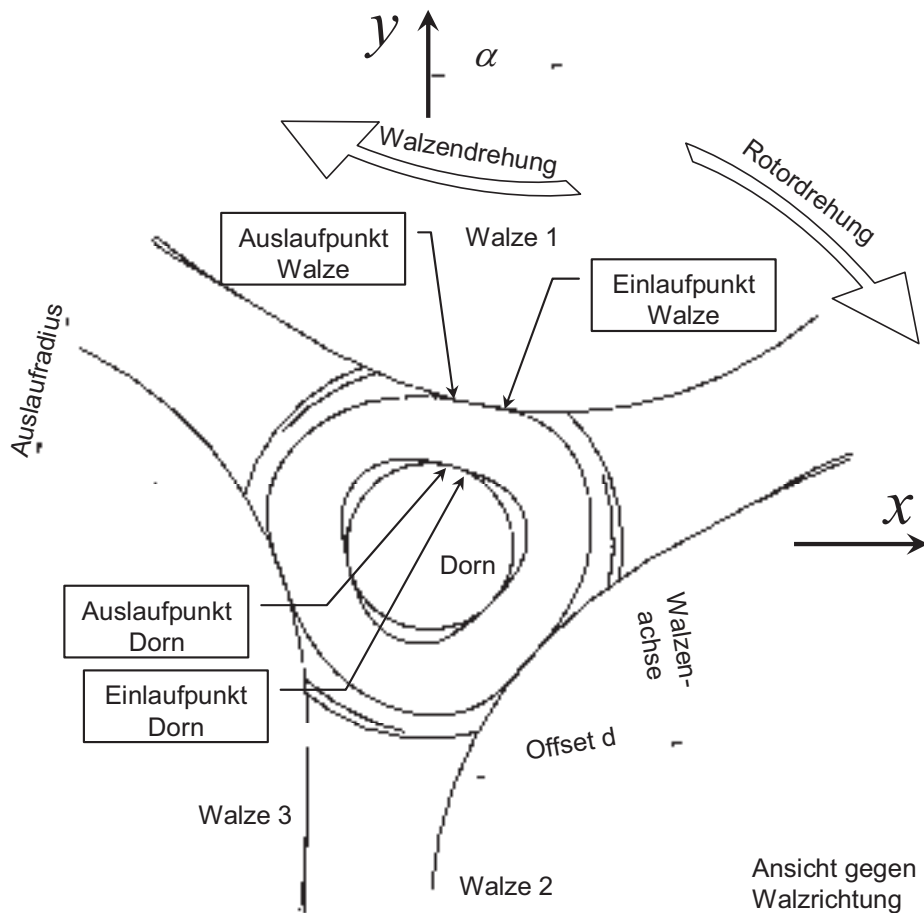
Schnitt durch das Walzgut quer zur Rohrachse
